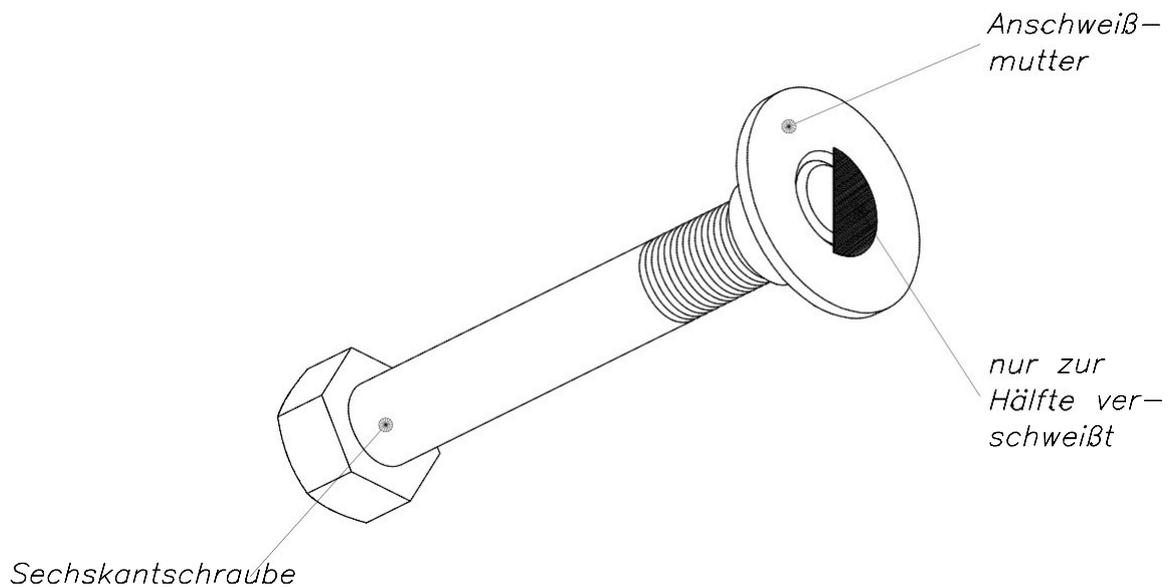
Beispiel einer inneren Verschweißung
